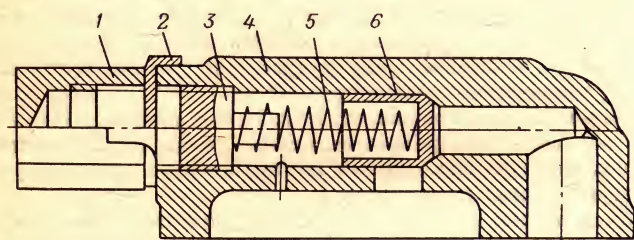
Сливной клапан двигателей СМД-60 и СМД-62:
